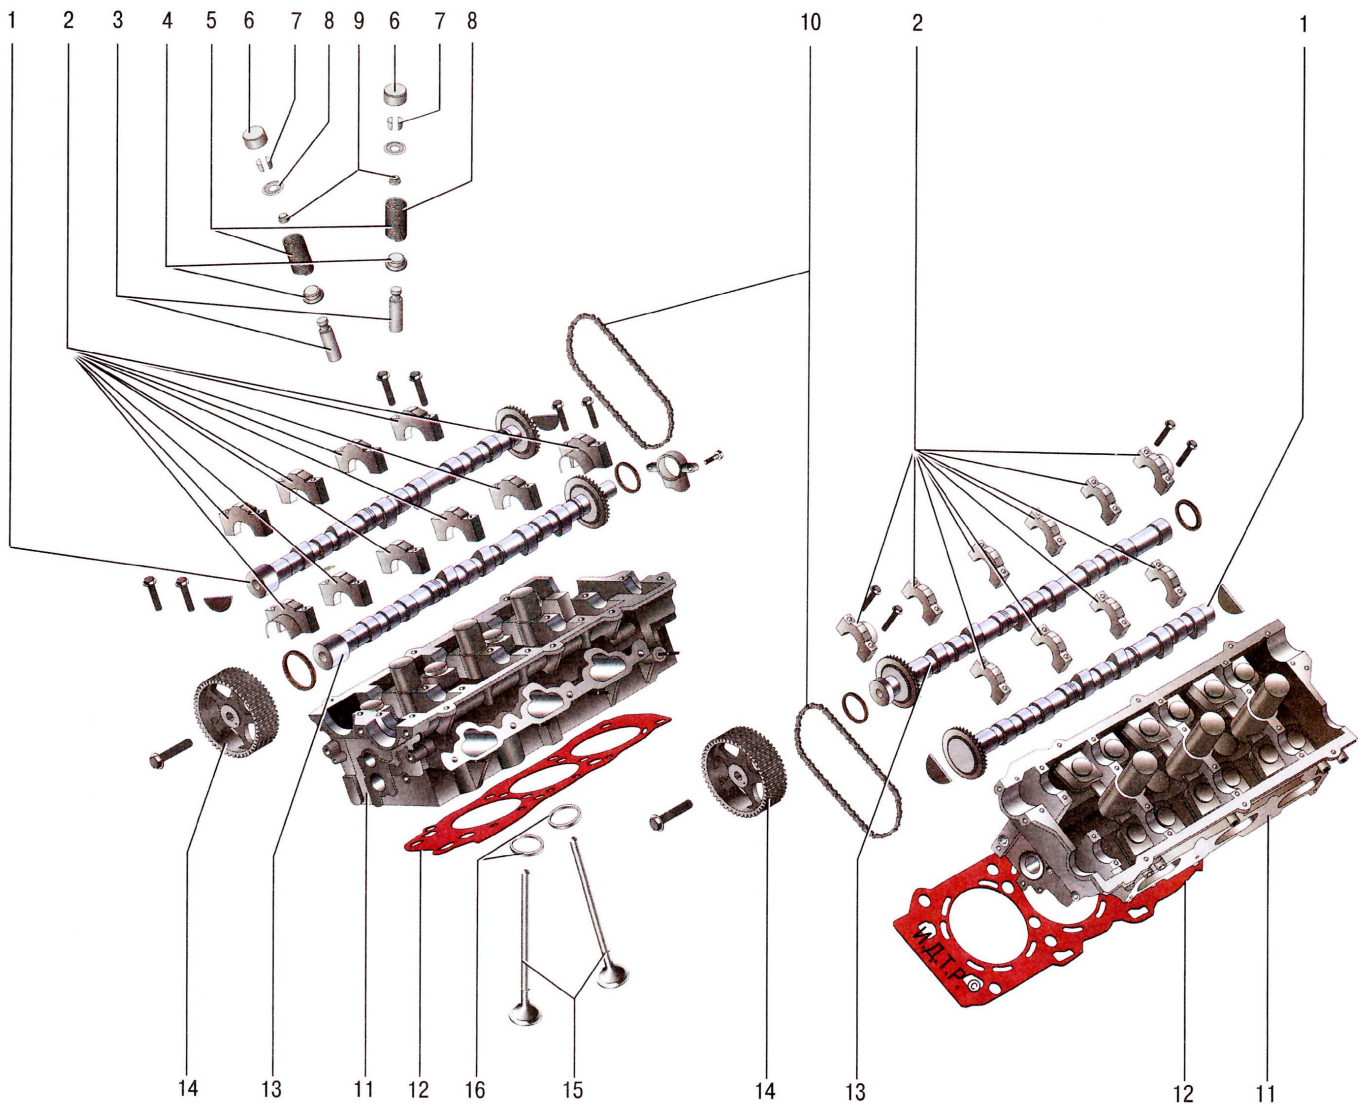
Головки блока цилиндров двигателя G6BA: 1 – выпускной распределительный вал; 2 – крышки подшипников распределительных валов; 3 – втулки клапанов; 4 – нижние тарелки пружин клапанов; 5 – пружины клапанов; 6 – гидротолкатель клапана; 7 – запорные сухари пружин клапанов; 8 – верхняя тарелка пружины клапана; 9 – маслосъемные колпачки; 10 – цепи привода выпускных распределительных валов; 11 – головка блока цилиндров; 12 – прокладка головки блока цилиндров; 13 – впускной распределительный вал; 14 – зубчатый шкив впускного распределительного вала; 15 – клапаны; 16 – седла клапанов
